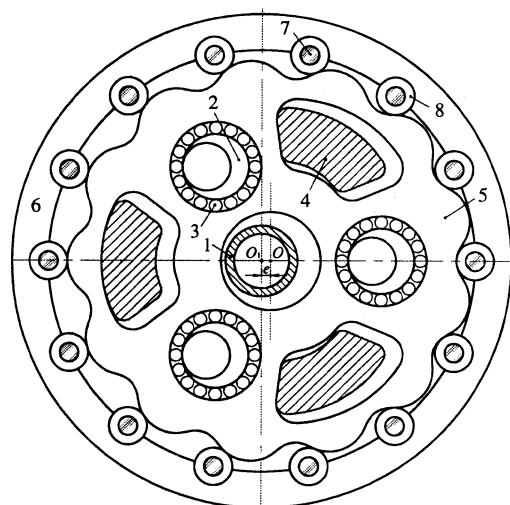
Поперечное сечение редуктора: 1 – входной вал; 2 – эксцентриковые валы; 3 – ролики подшипника; 4 – пальцы выходного вала; 5 – сателлит; 6 – обойма; 7 – втулки; 8 – цевки
